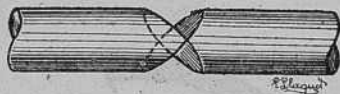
Preparación para la soldadura de barras redondas de un diámetro superior a 15 mm.
